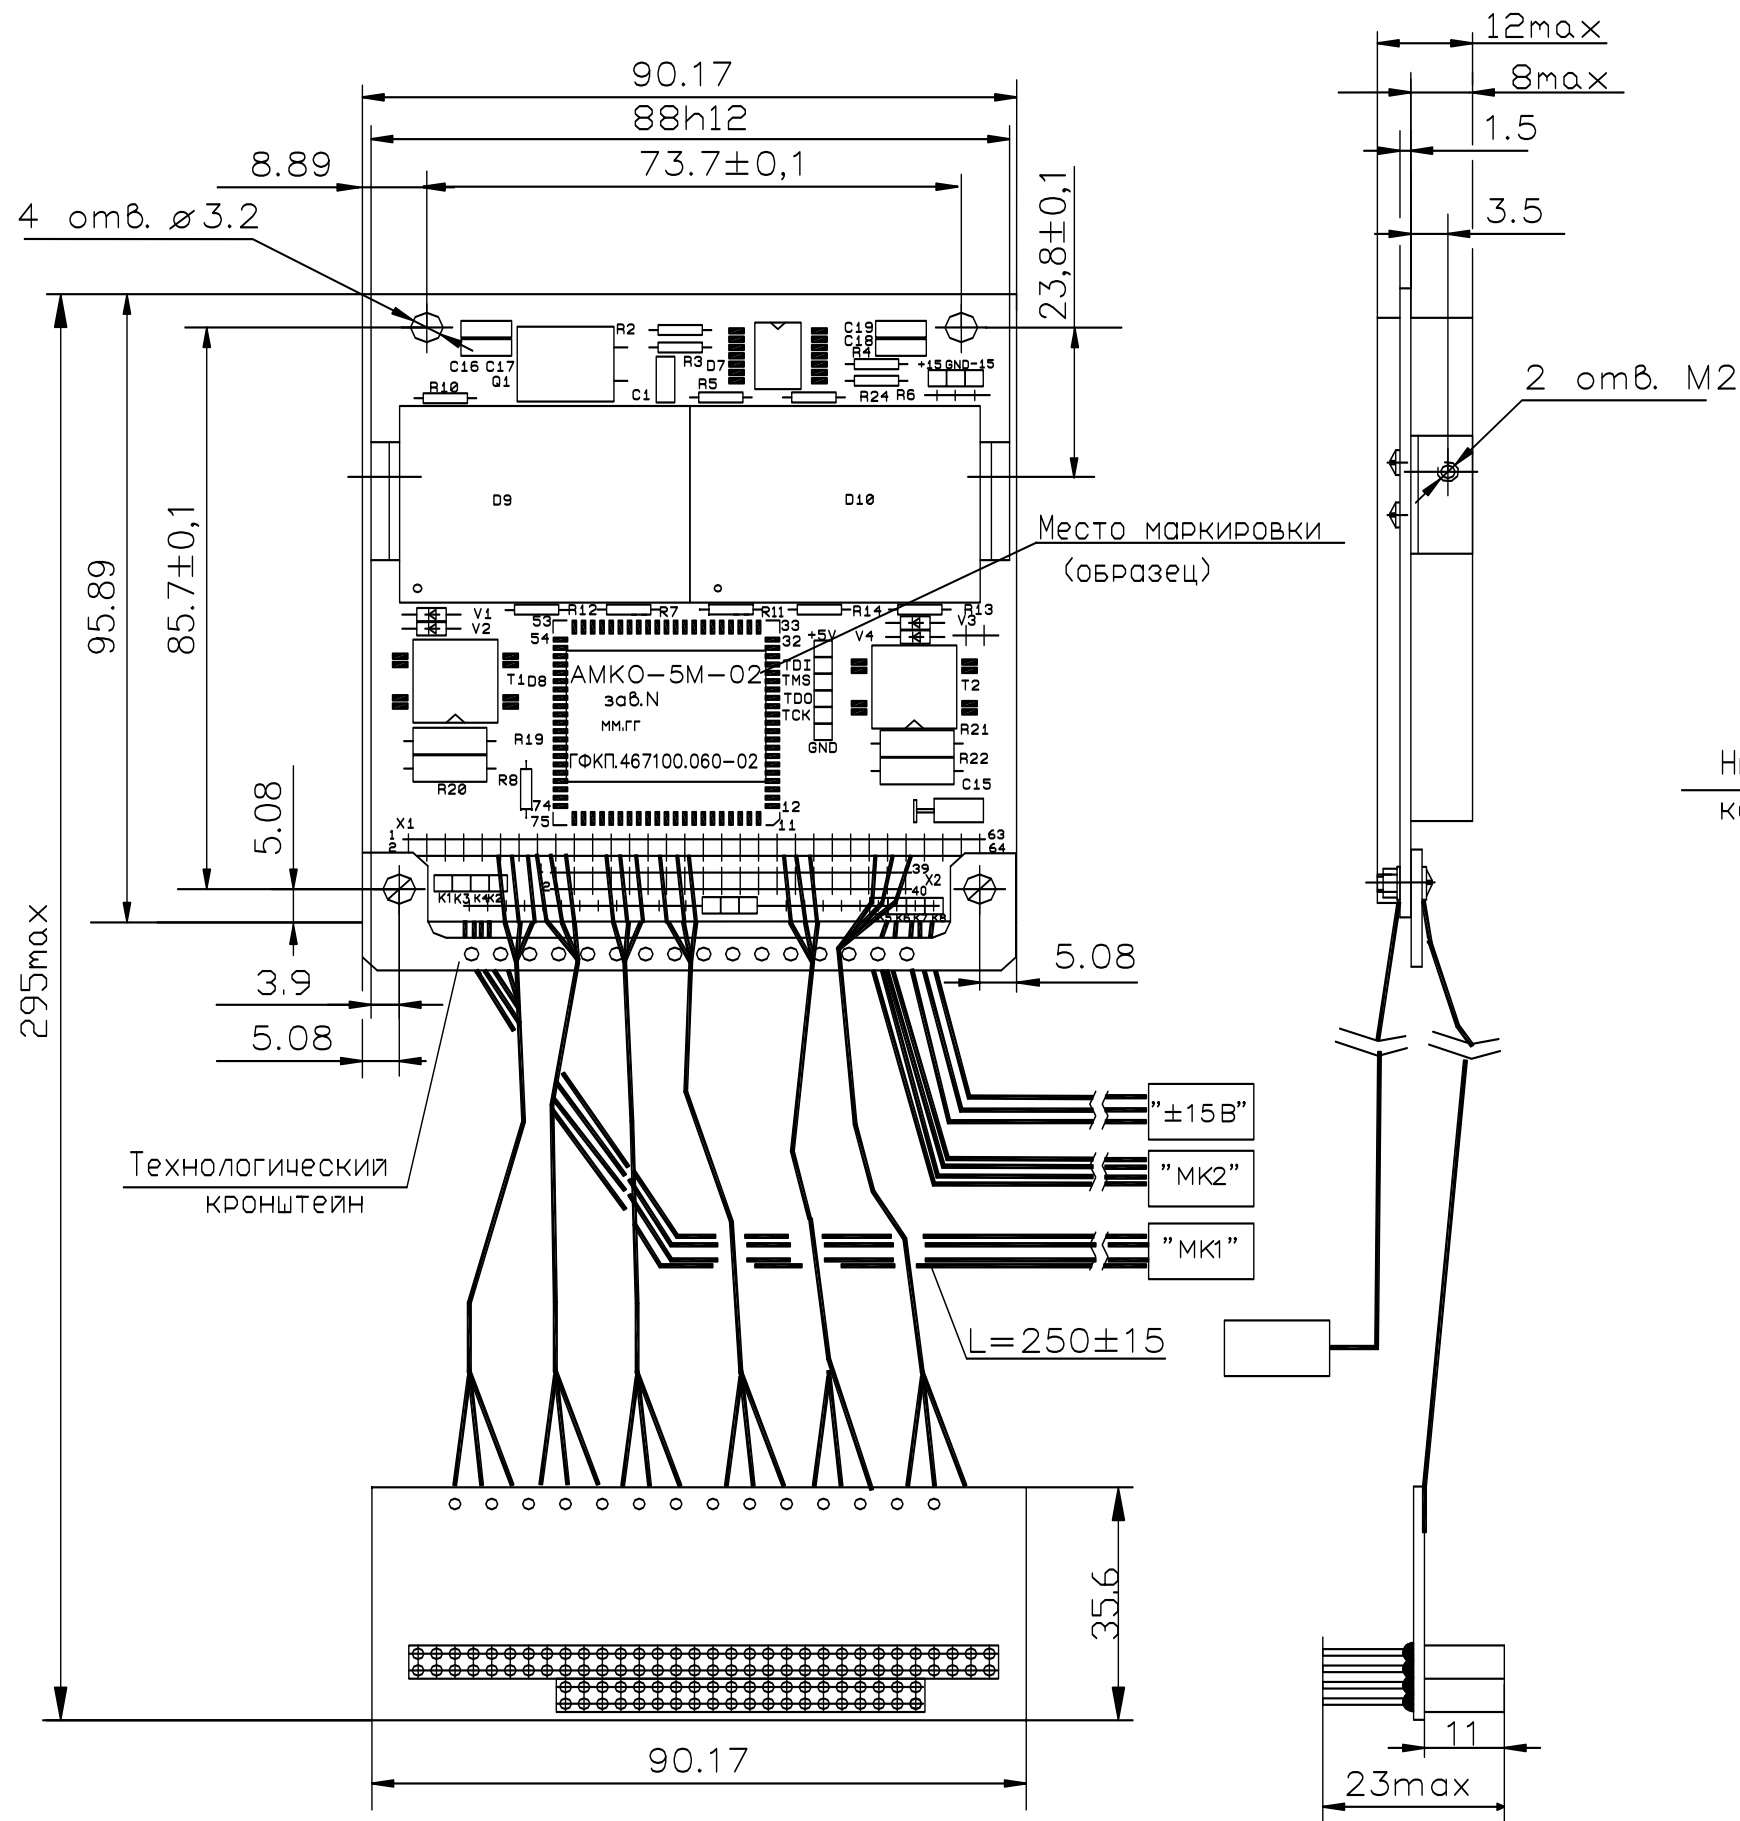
Габаритный чертеж исполнения АМКО-5М-02
